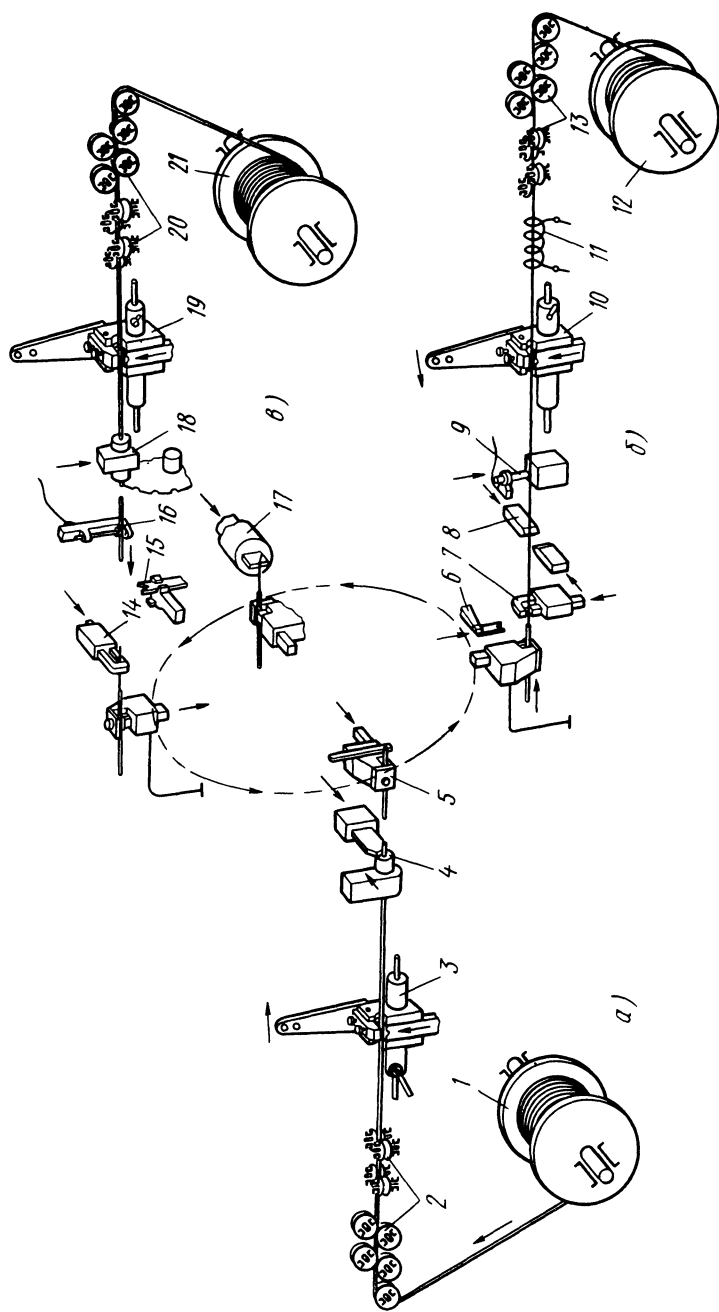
Изготовление трехжильных выводов на автомате контактной стыковой сваркой:
